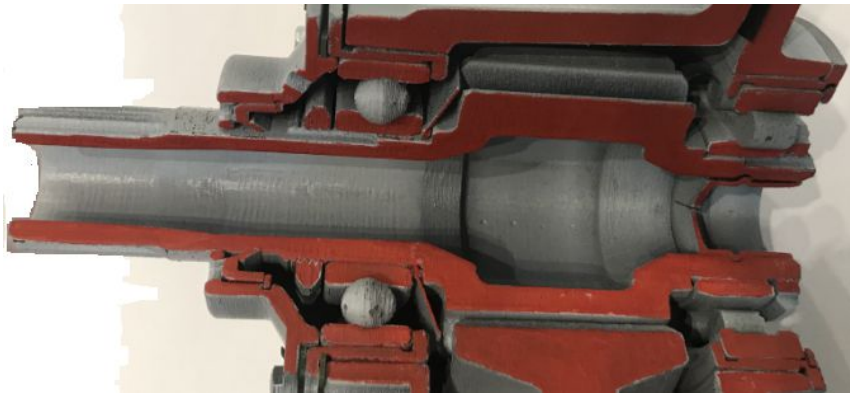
Модуль входного вала редуктора с вырезом четверти
